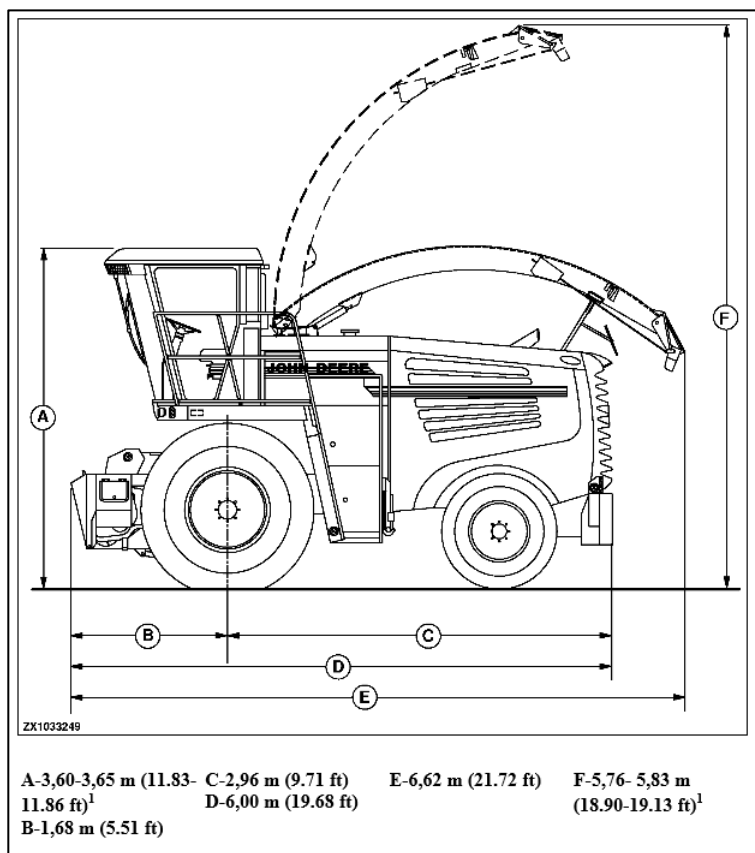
Dimensions des fourragères John Deere, modèles 7200, 7300, 7400, 7500, 7700 et 7800. Vue de côté.
